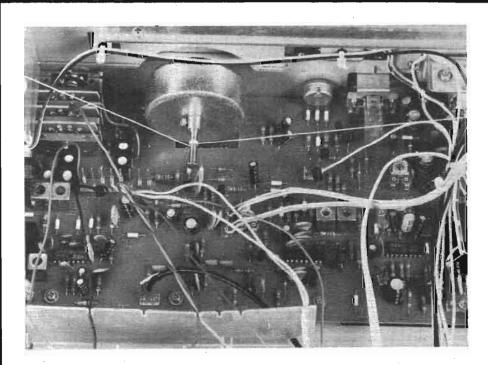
Photo A. – A première vue rien ne distingue les appareils made in France de ceux construits en extrême- Orient.
